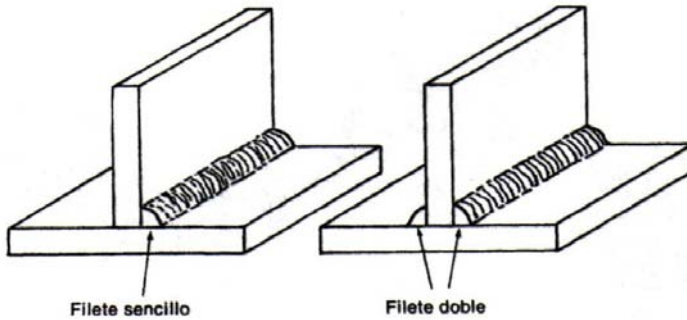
Soldaduras de filete sencillo y de filete doble
